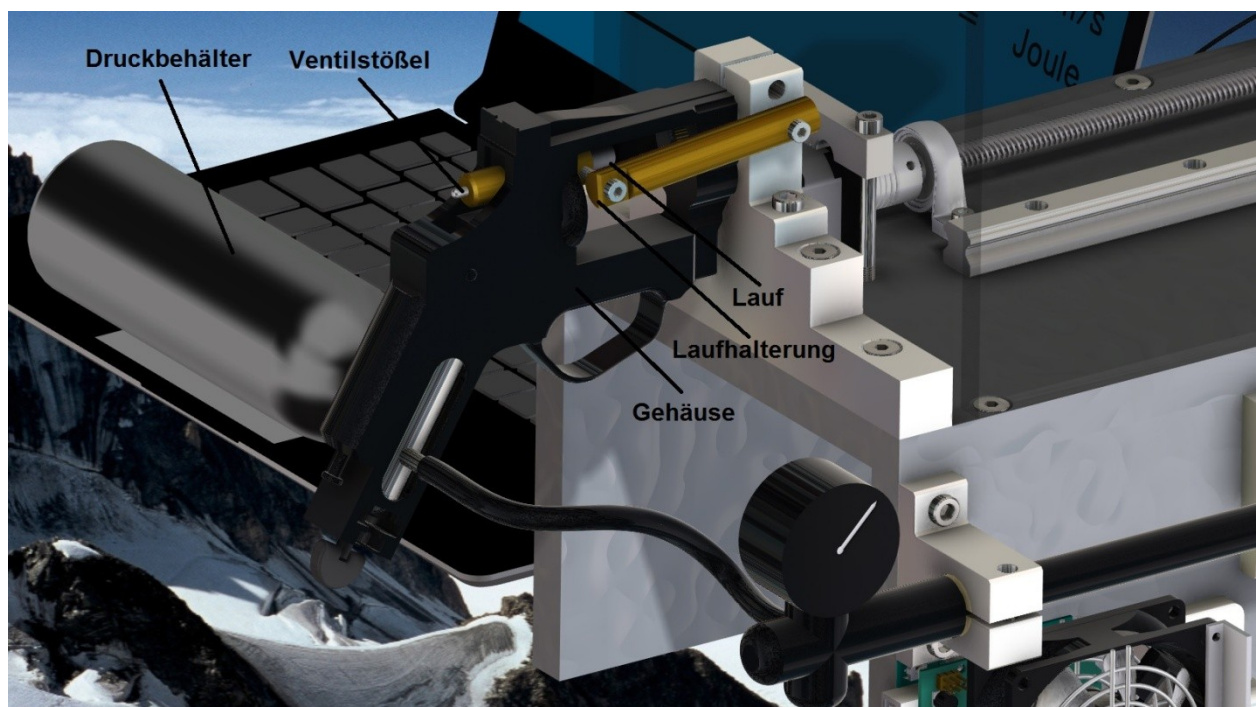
Detailansicht der 3D-Konstruktion im Bereich der Schussabgabe
